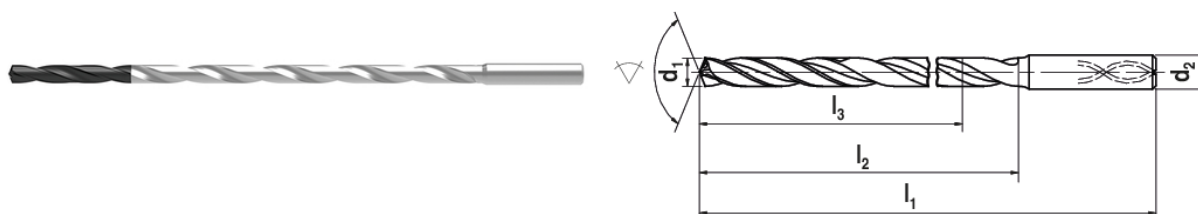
Nástroj operace Vrták D5 pro M6 [10]
